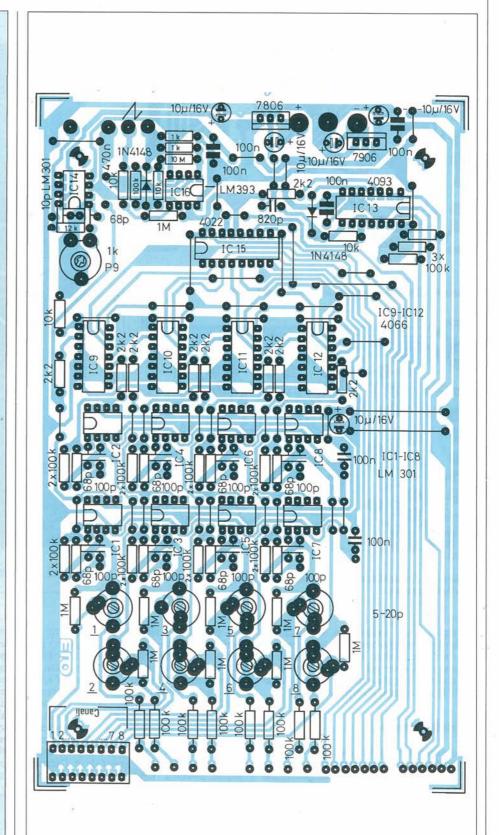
Disposizione dei componenti sul circuito stampato generale.
